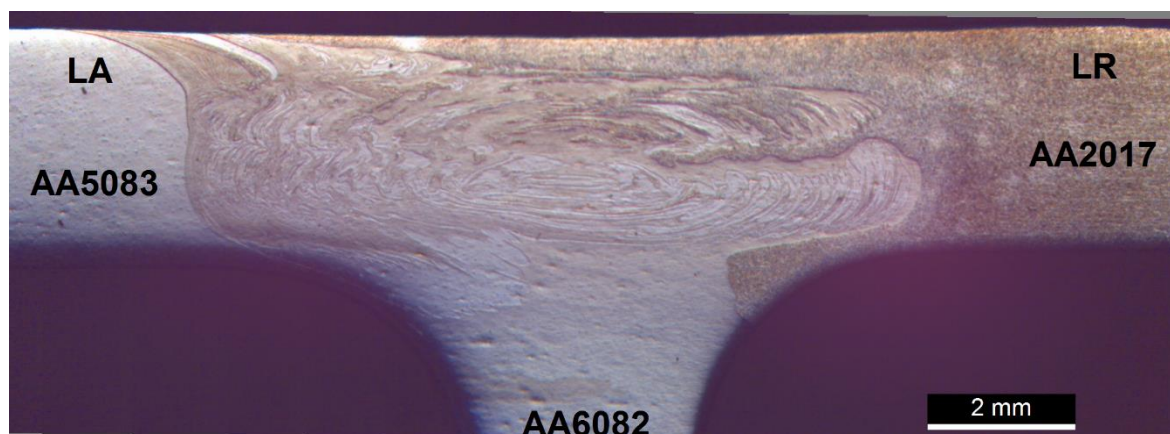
Macrografia da soldadura 562BRP-3
